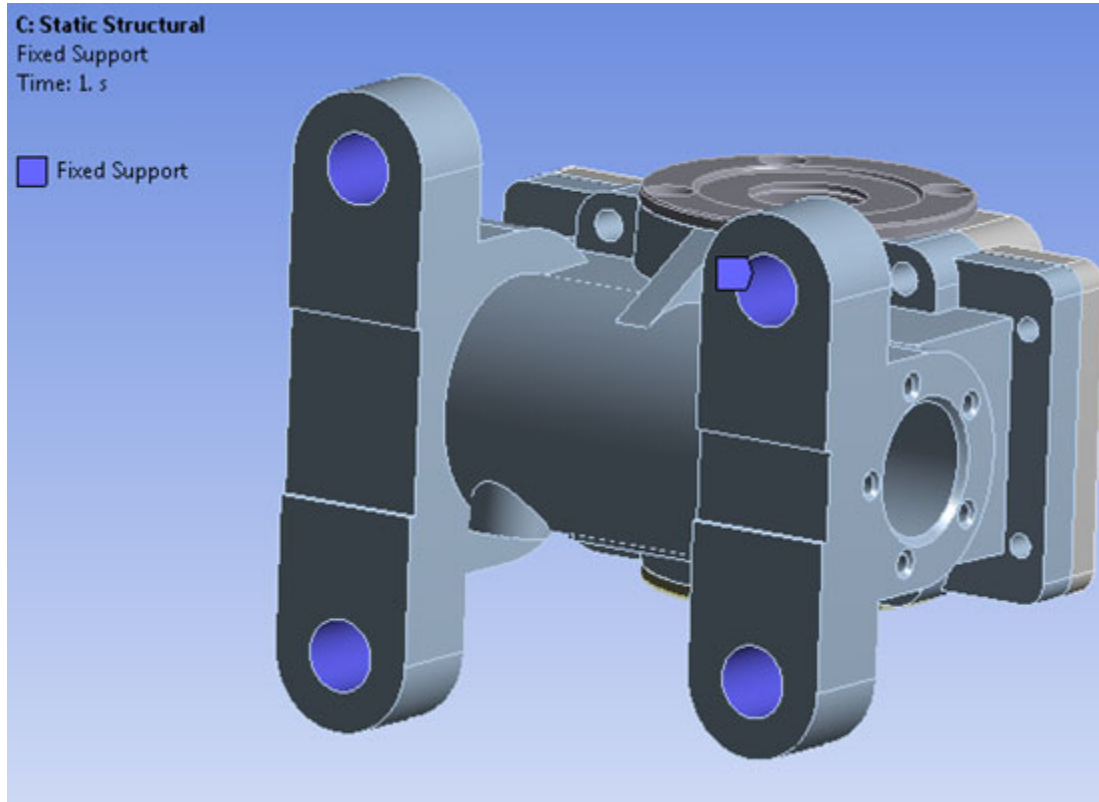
Фіксація корпусу редуктора відповідно ко кінематичної схеми
